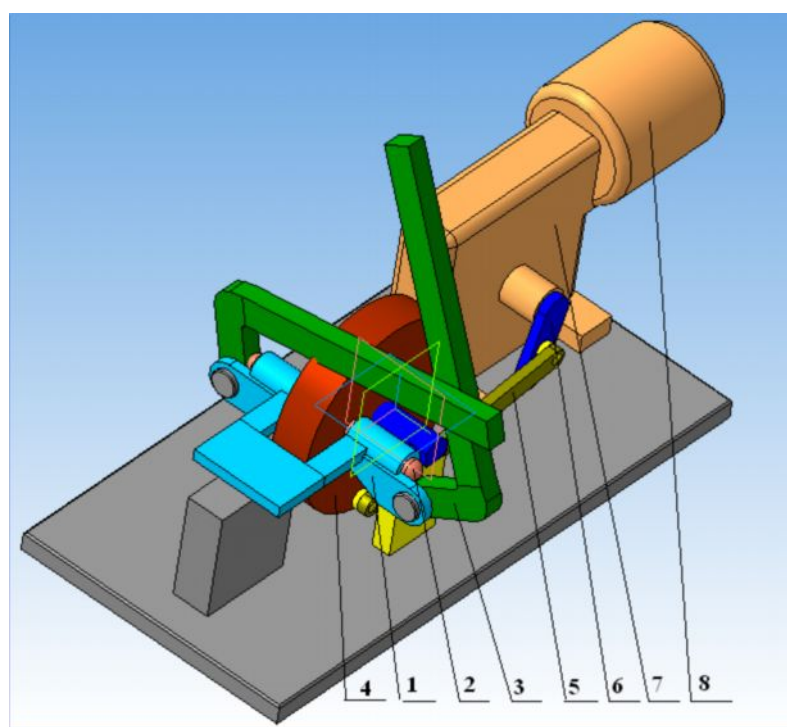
Схема устройства для испытаний с нагрузочными рычагами, установленными непосредственно на суппорт
